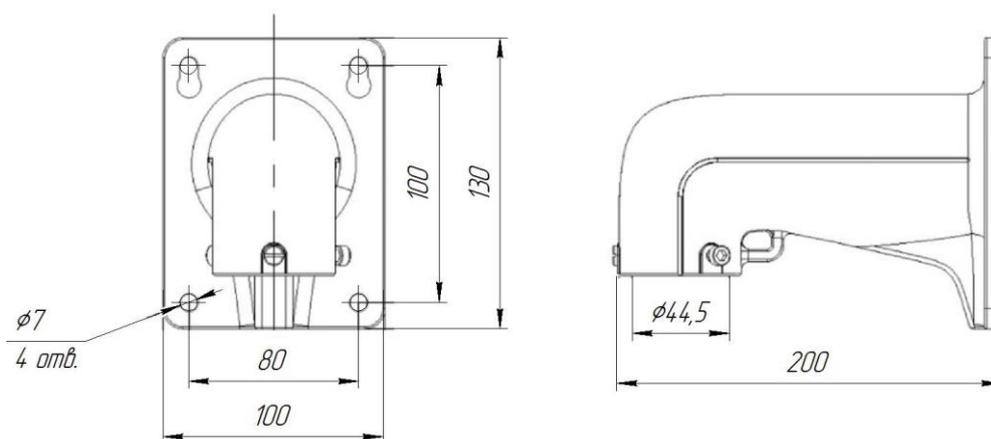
Габаритные размеры кронштейна IP-видеокамеры SDP-825
